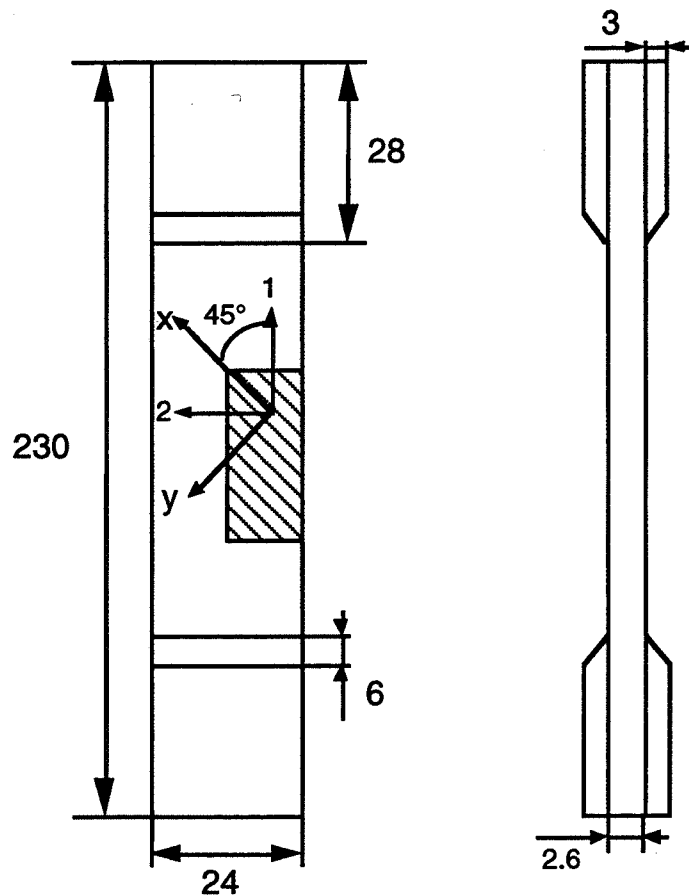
Dimensions des éprouvettes hors-axes à 45°.
